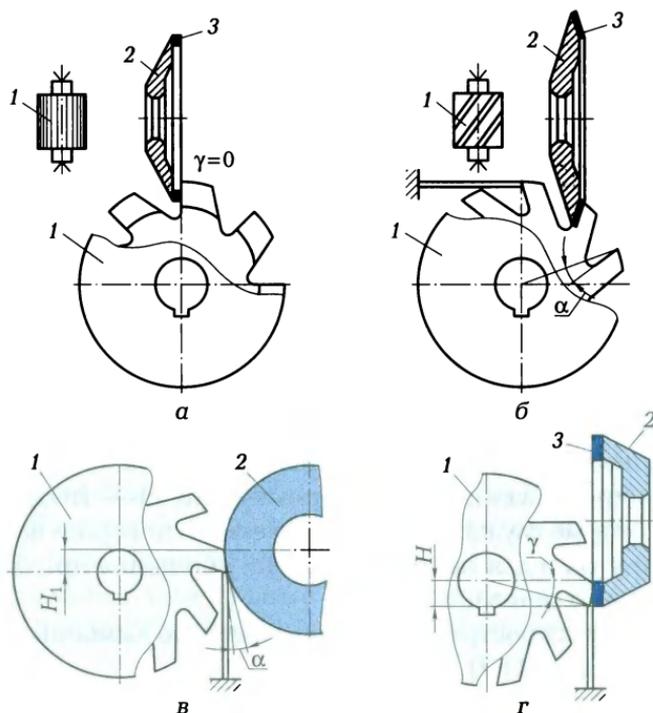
Схемы заточки фрез по передней (а, б) и задней (в, г) поверхностям:
